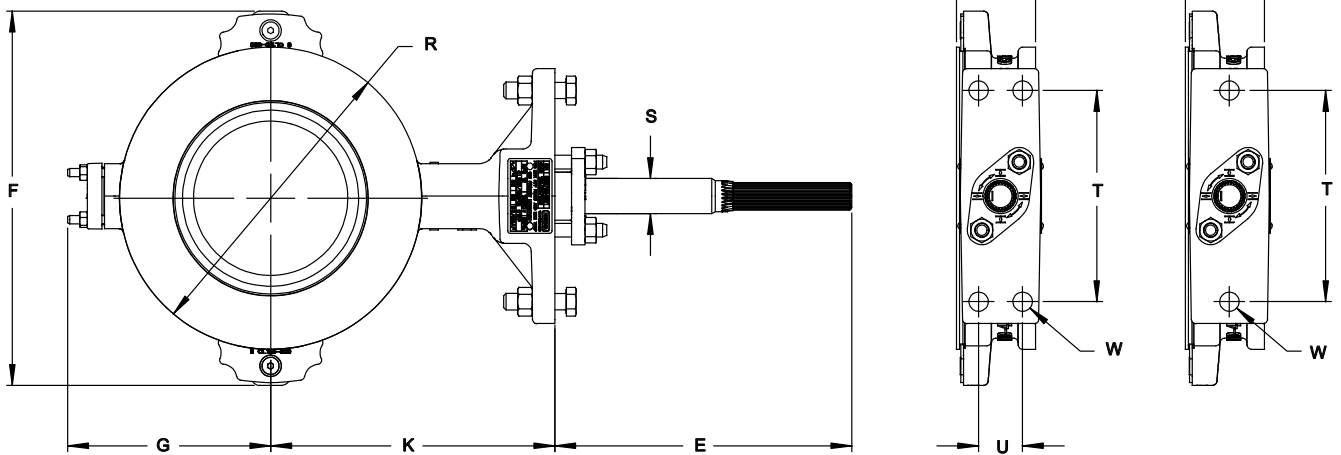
Размеры затвора Control-Disk в бесфланцевом корпусе
